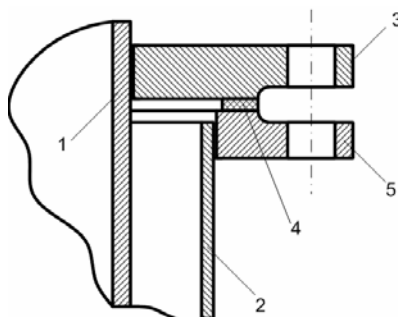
Конструкция разъемного крепления рубашки к корпусу сварного аппарата:
